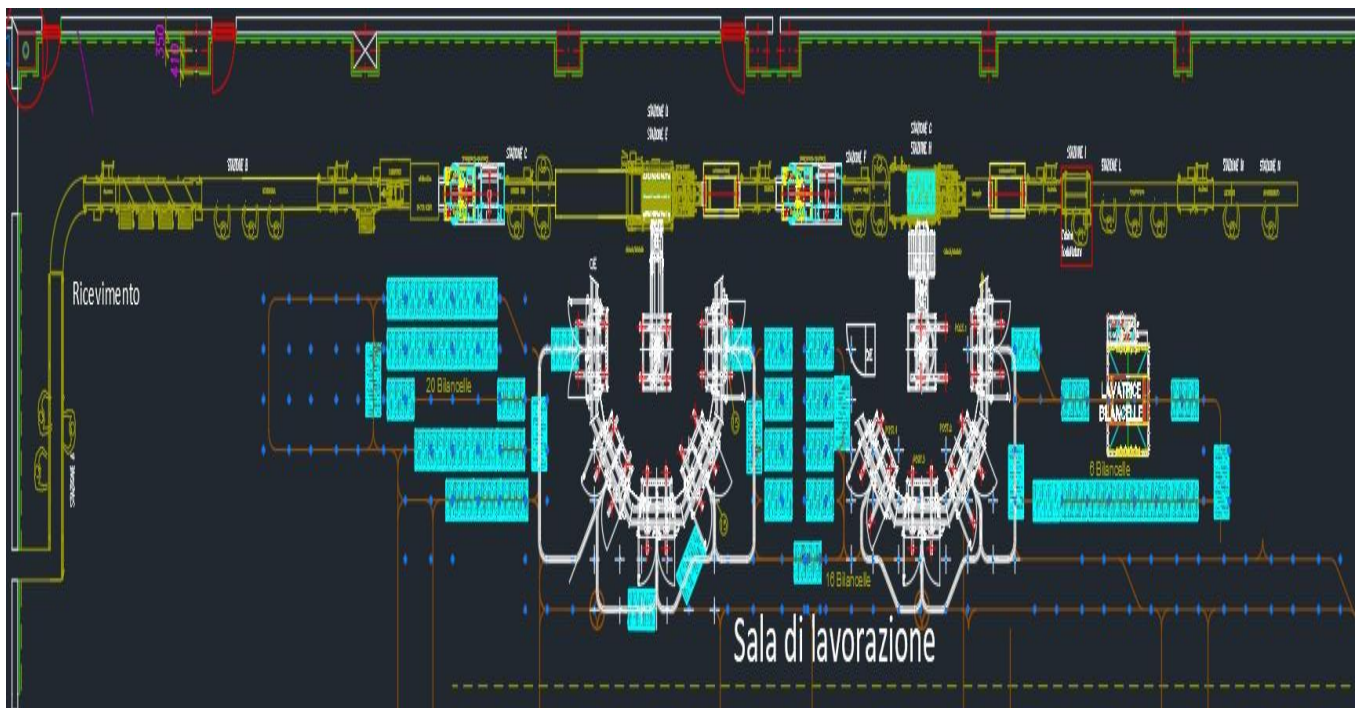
Layout completo dell'impianto con i robot nelle stazioni di carico/scarico
